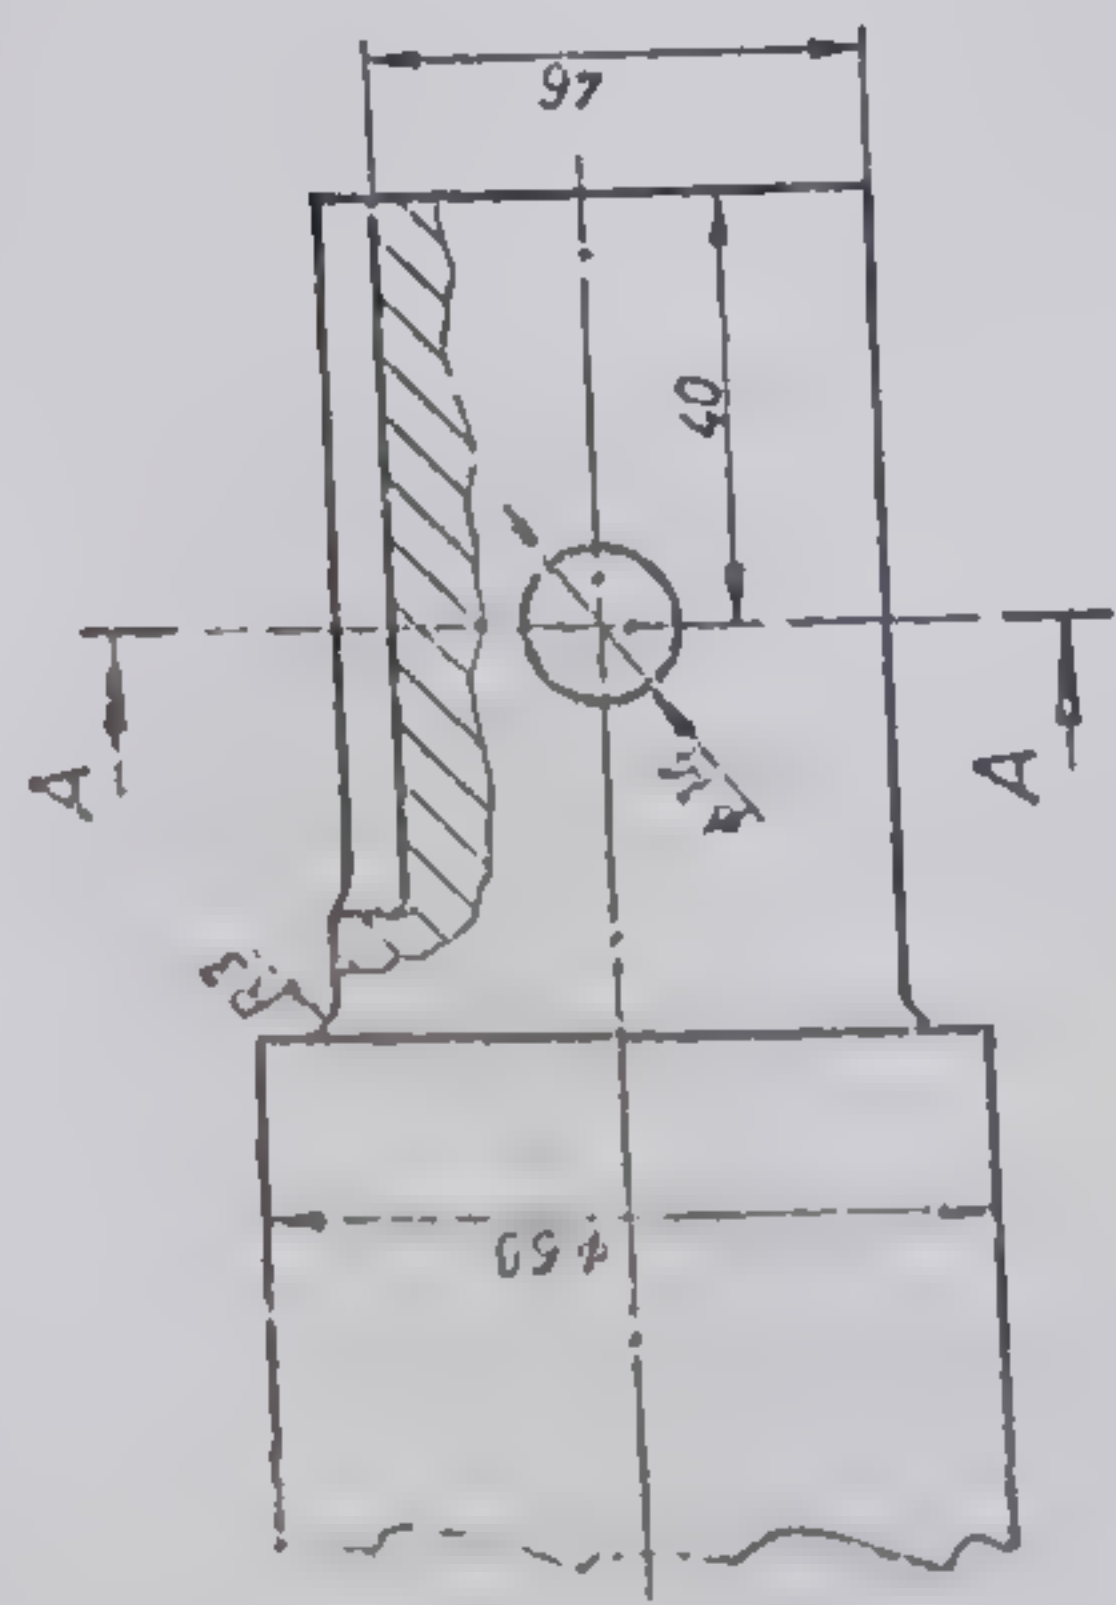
Secțiune frontală într-o piesă cu flanșă cilindrică (problemă).
